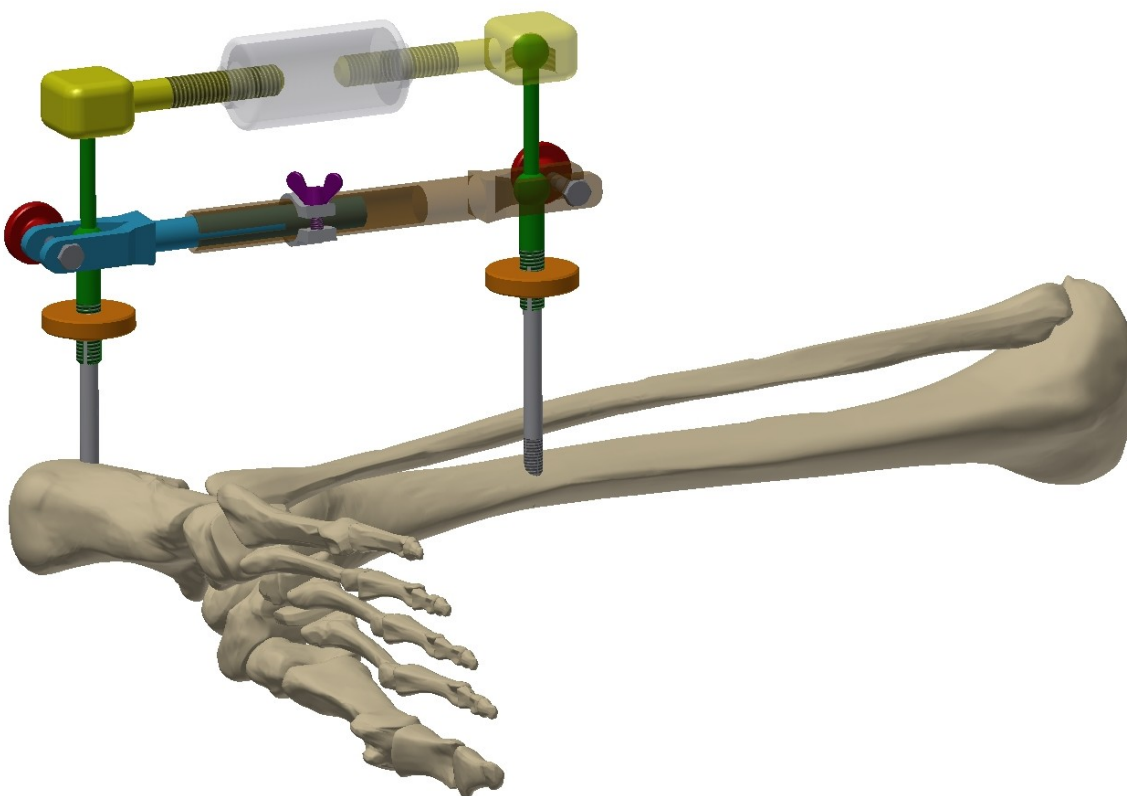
Umístění přípravku - varianta č. 3 - Typ II.
